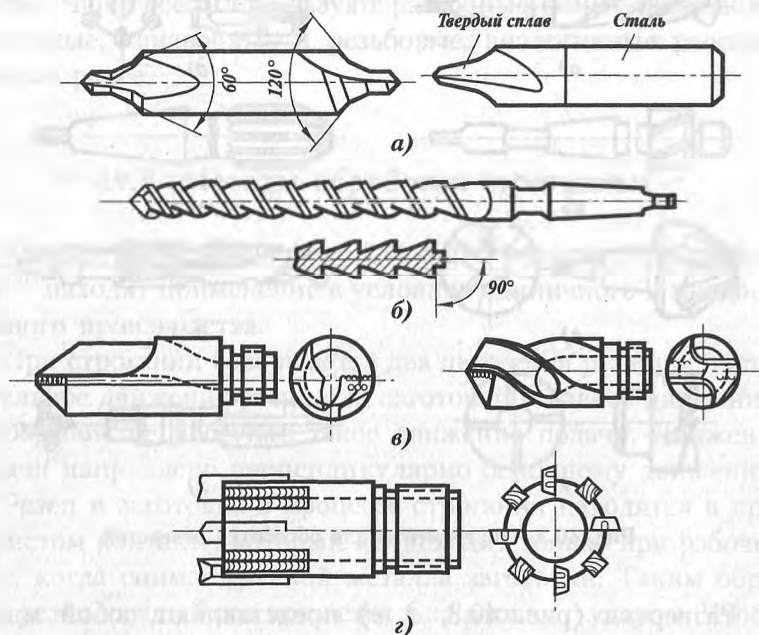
Специальные сверла: а — центровочное; б — шнековое; в — ружейное; г — кольцевого сверления
